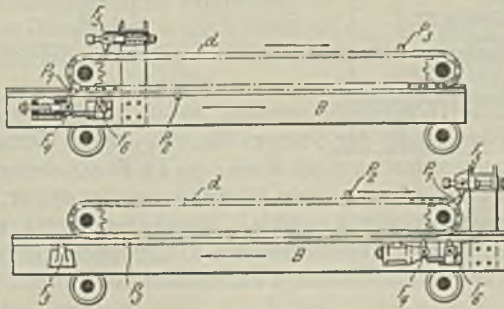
Planierstangenantrieb der Sächsischen Maschinenfabrik.
